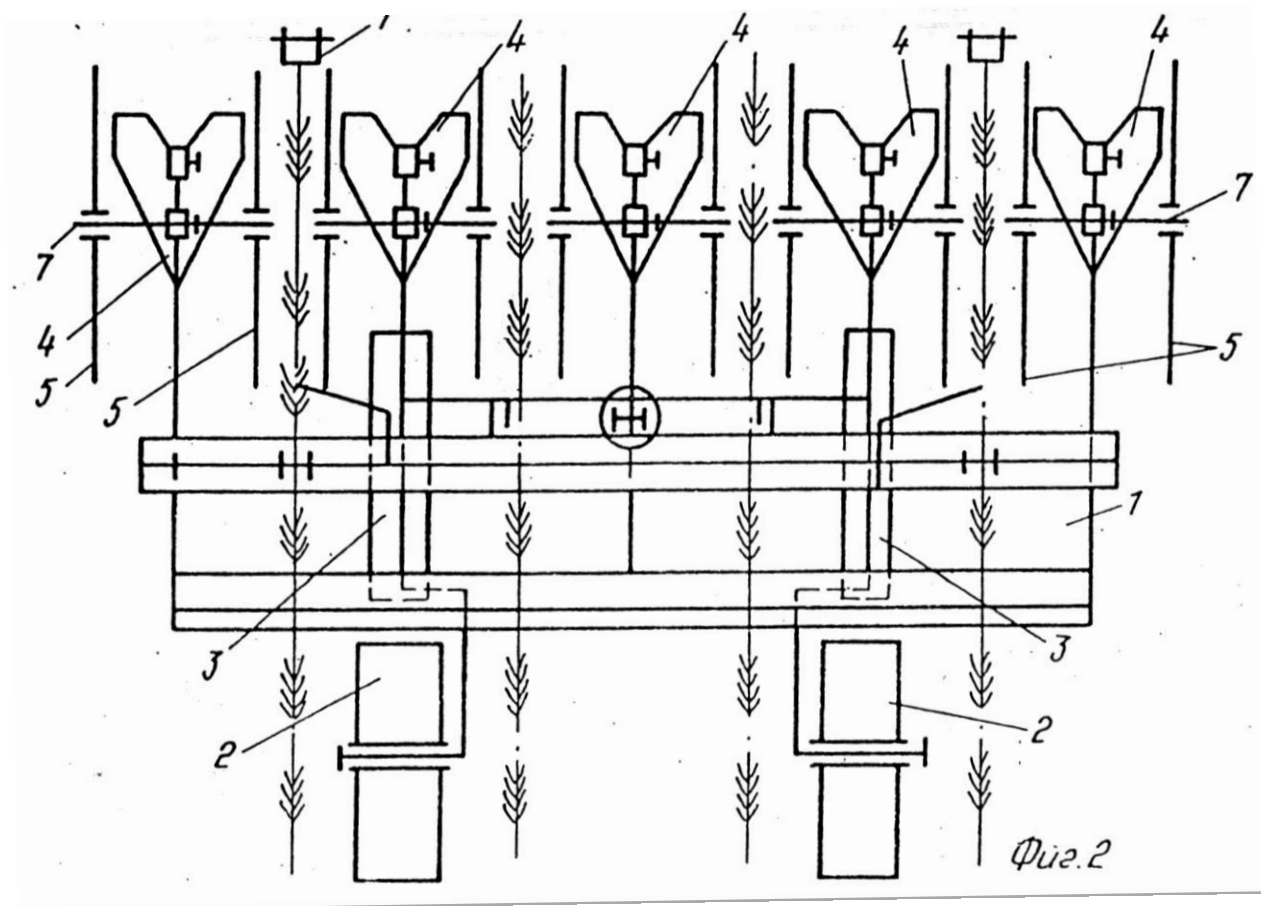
Схема культиватора для міжрядного обробітку рослин
